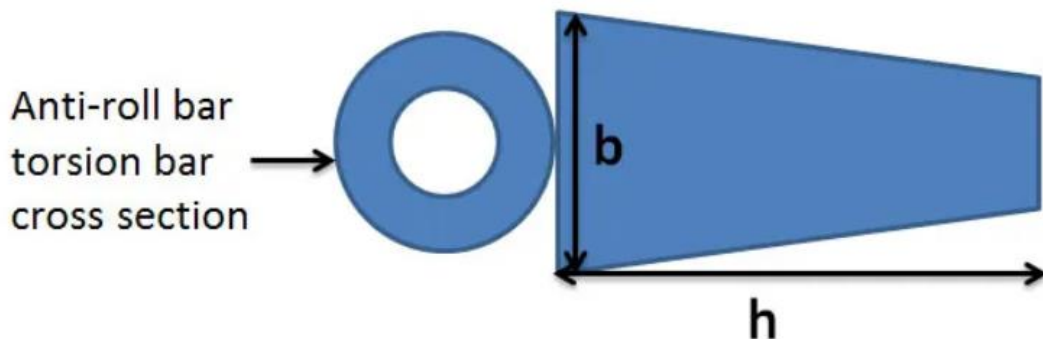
Vista en planta de la barra estabilizadora en el modo de rigidez “dura”
